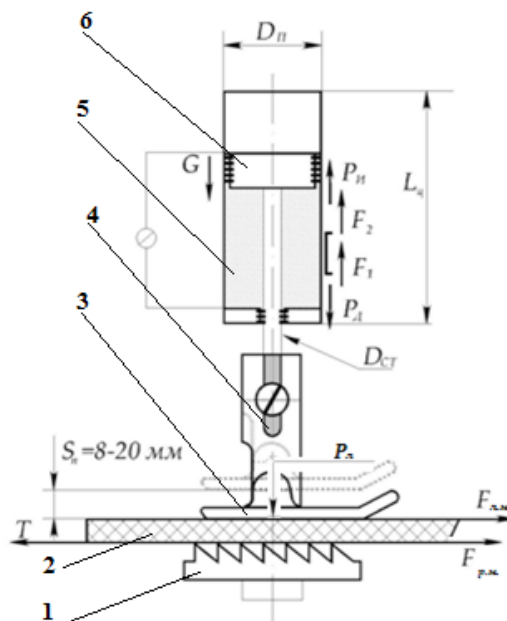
Схема нового узла лапки с гидроприводом: 1 — зубчатая рейка; 2 — материал; 3 — лапка; 4 — стержень; 5 — гидроцилиндр; 6 — поршень
